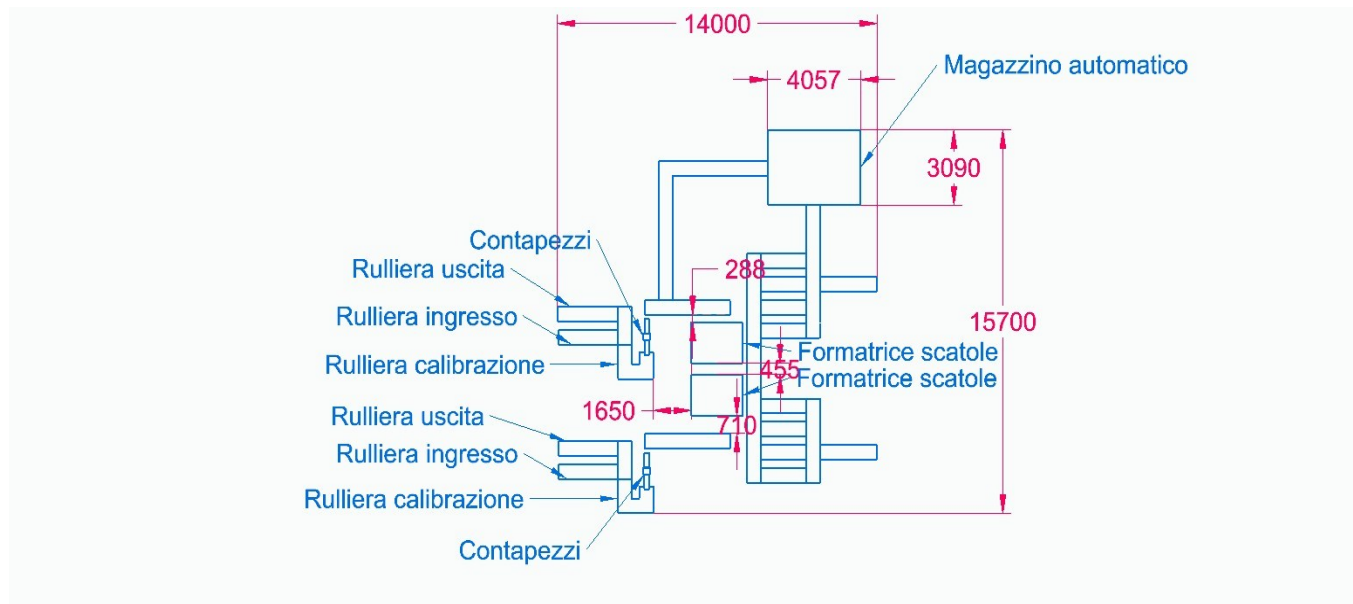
prima soluzione per il layout del nuovo impianto di imballaggio. Dimensioni in millimetri
